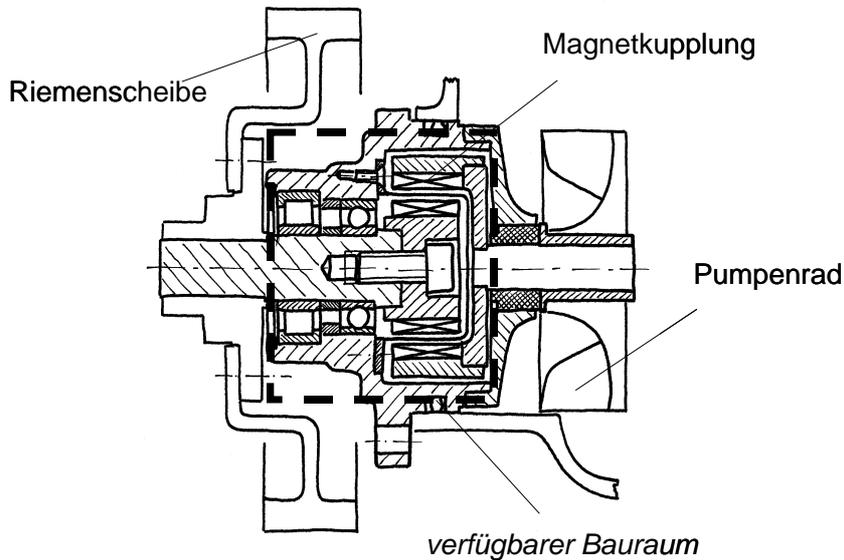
Kühlmittelpumpe mit berührungsloser Drehmomentübertragung auf das Pumpenrad
